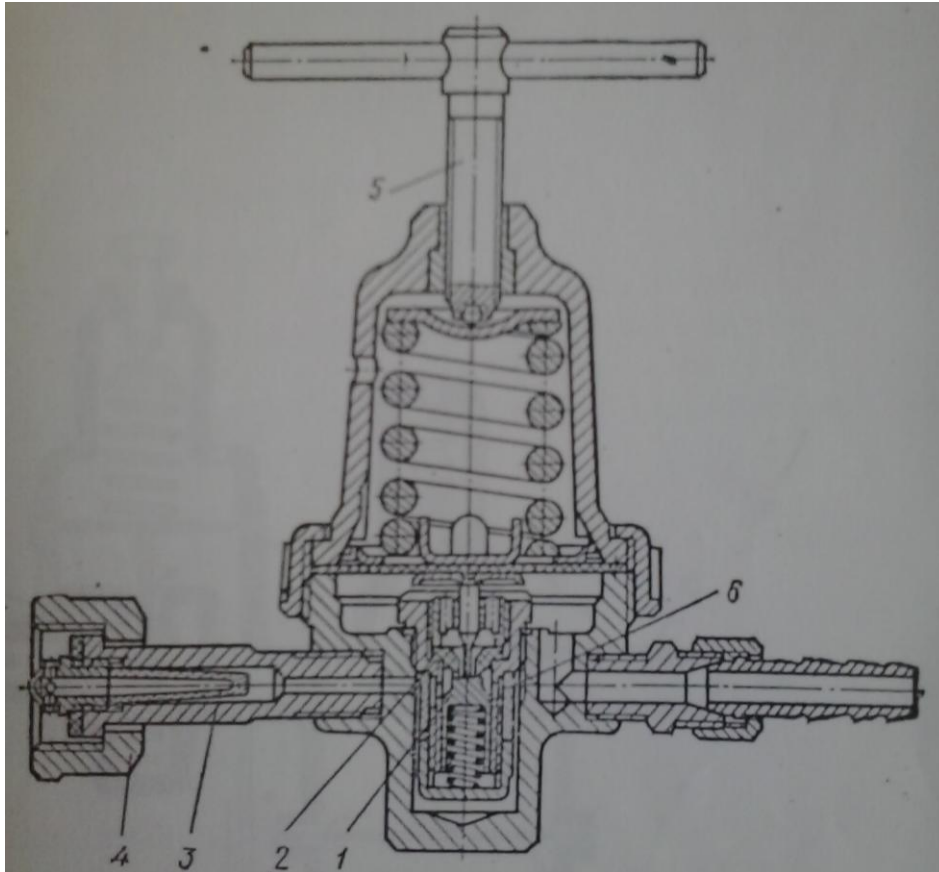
Схема кисневого редуктора ДКП – 2 – 78
